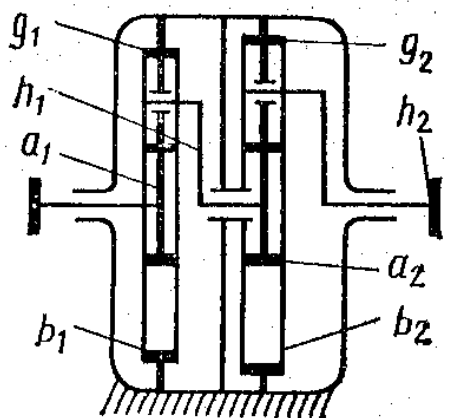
Схема двухступенчатого планетарного редуктора
